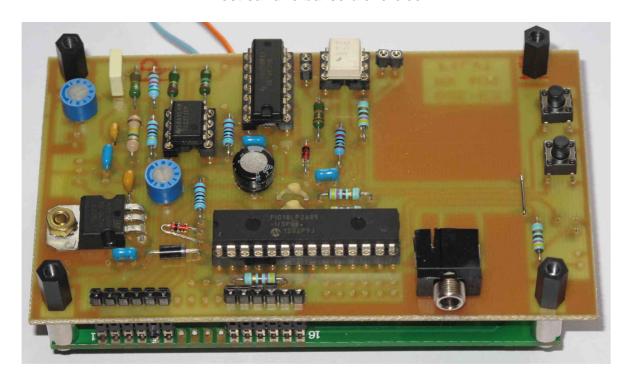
Autre version en vue de dessous, le plan de masse à coté du PIC é été utilisé pour placer le connecteur Jack 3,5 de l'entrée du signal
